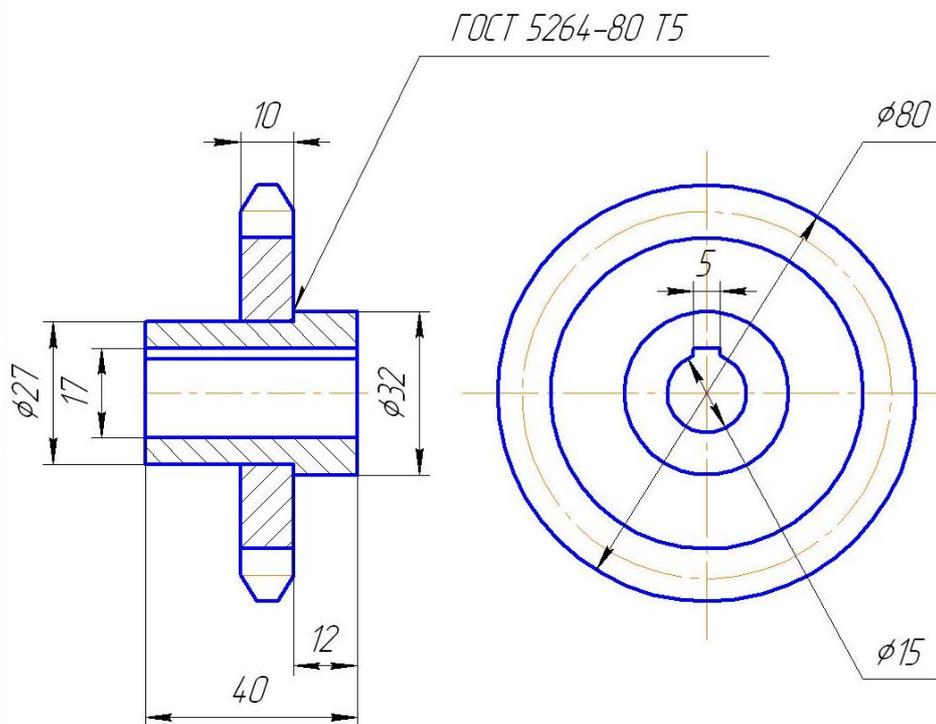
Тавровое сварное соединение, выполненное ручной дуговой сваркой
